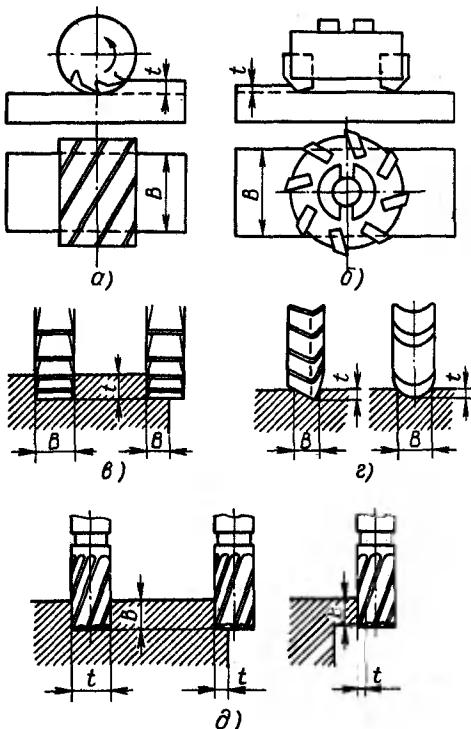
Глубина и ширина фрезерования для различных типов фрез:
